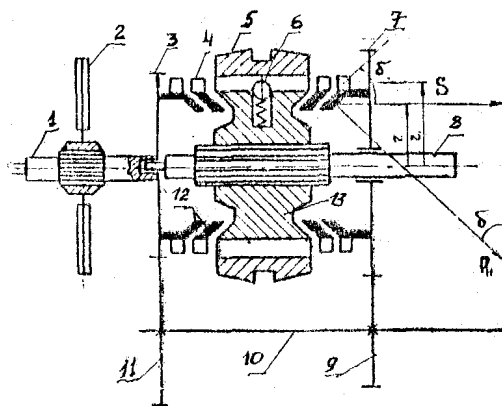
Синхронізатор: 1 – первинний ведучий вал коробки передач; 2 – ведений диск зчеплення; 3 – шестірня первинного вала постійного зчеплення; 4 – блокувальне кільце; 5 – муфта; 6 – фіксатор; 7 – шестірня IV передачі; 8 – вторинний (ведений) вал; 9 – шестерня проміжного вала постійного зчеплення IV передачі; 10 – проміжний вал; 11 – шестерня проміжного вала постійного зчеплення; 12 – кончні поверхні блокувального кільця і шестерні первинного вала; 13 – маточина
